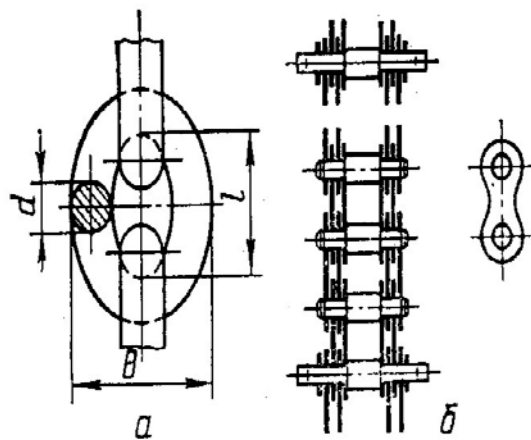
Цепи: а – сварные; б – пластинчатые
